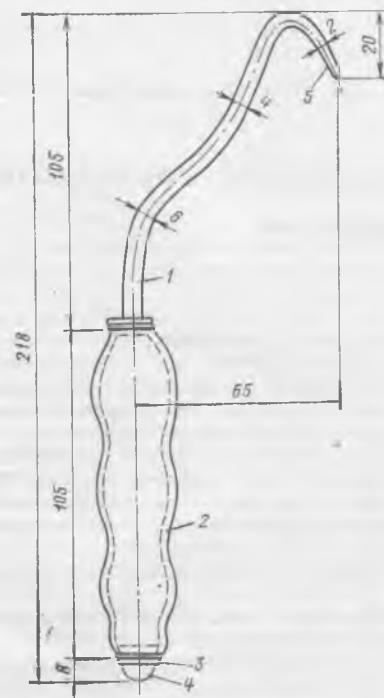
Ручной инструмент для вязки арматурных конструкций
